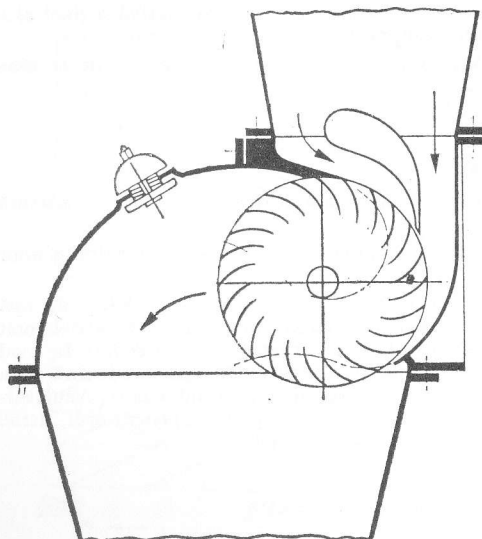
Secțiunea prin rotor și aparatul director la o turbină cu trecere directă.
